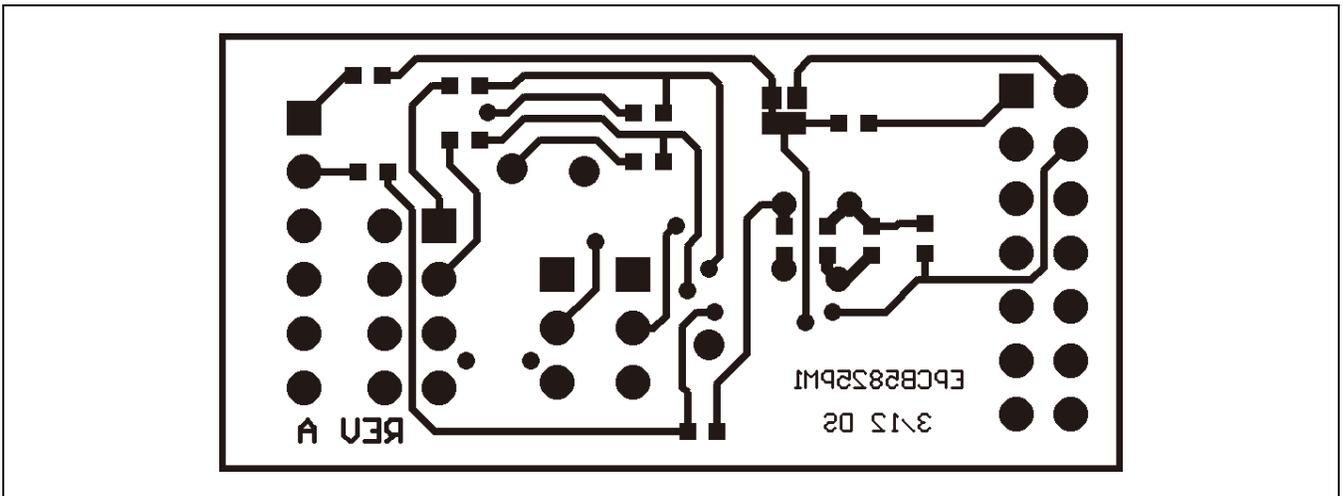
MAX5825PMB11外设模块PCB布局——焊接层
